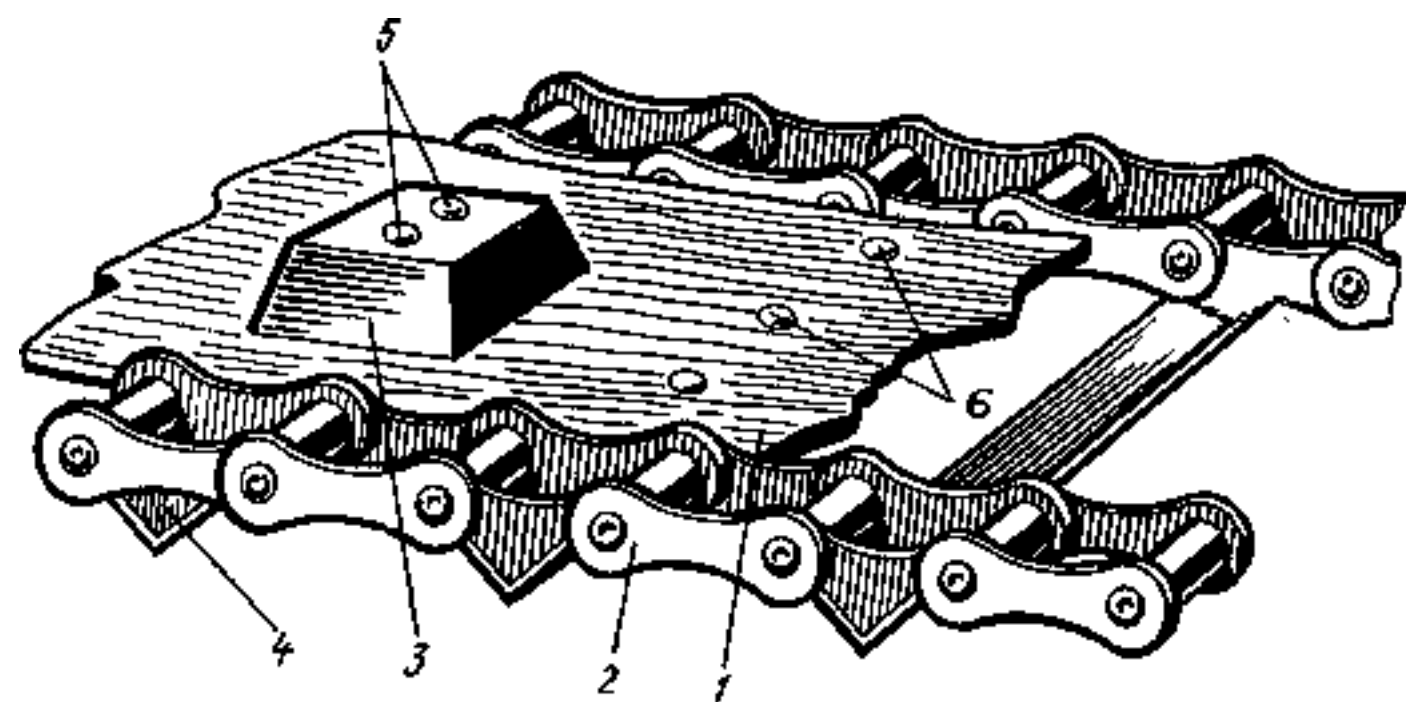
Схема устройства резинометаллической гусеницы вездехода:
